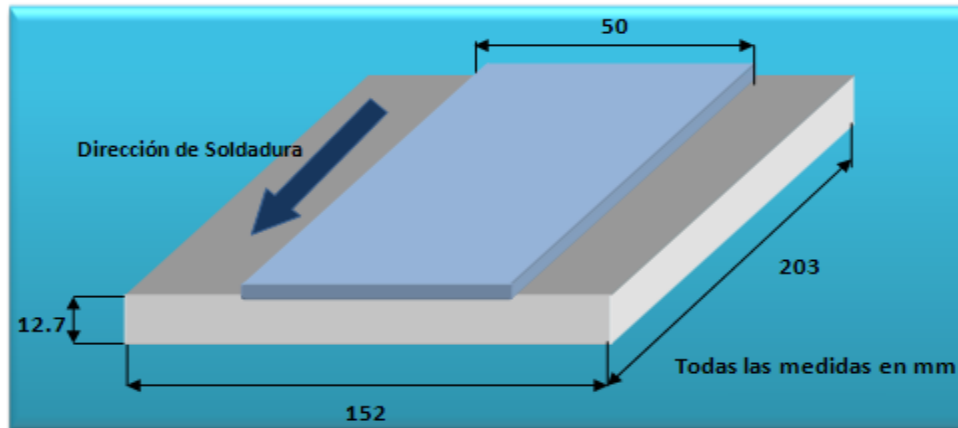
Medidas del cupón de soldadura para calificar revestimientos
